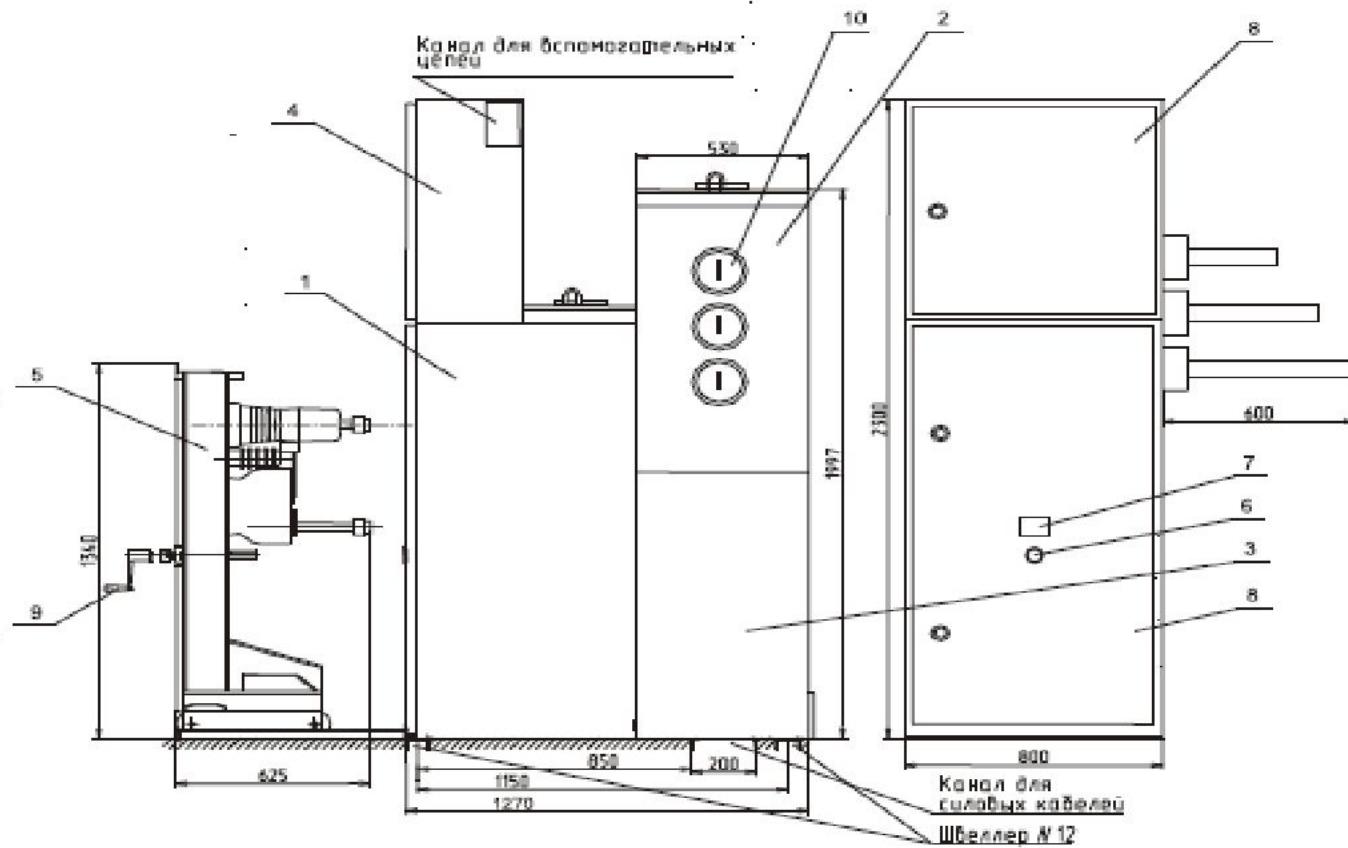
Габаритные и установочные размеры шкафа КРУ К-Ин97
